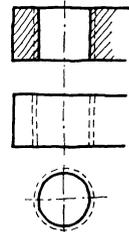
Muttergewinde (Schnitt, Ansicht, Draufsicht).
